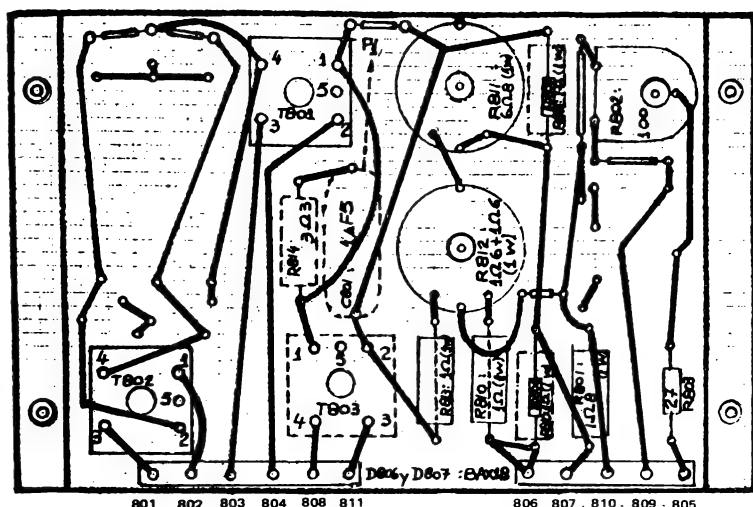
Vista del lado componentes de la plaqueta impresa que contiene el conjunto compensador de tolerancias.
